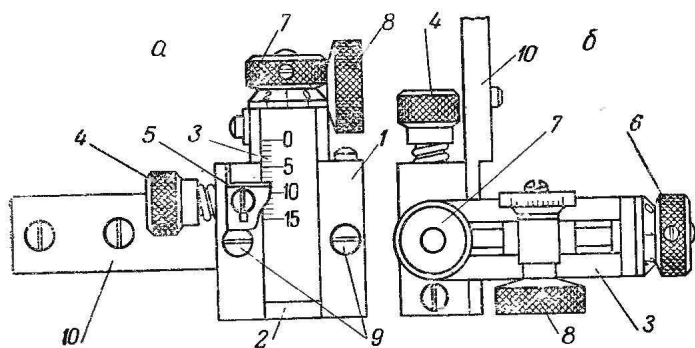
Диоптрический прицел: а — вид сбоку; б — вид сверху; 1 — основание прицела (колонка); 2 — вертикальный фигурный паз; 3 — угольник; 4 — стопорный винт с пружиной; 5 — паз для крепления передвижного показателя; 6 — микрометрический винт горизонтальных поправок; 7 — микрометрический винт вертикальных поправок; 8 — тарель; 9 — винты крепления с переходной планкой; 10 — переходная планка
